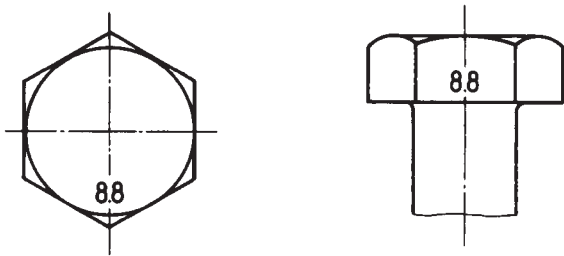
Beispiele für die Kennzeichnung von Sechskantschrauben
